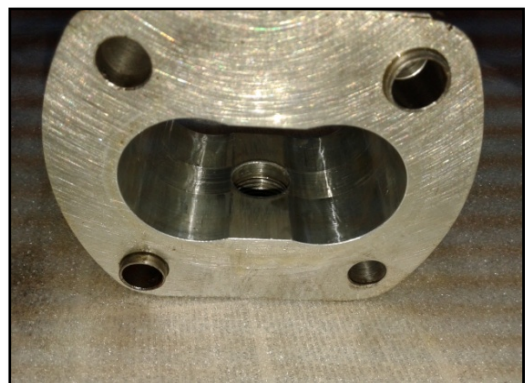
Desgaste en cuerpo de bomba de engranajes.
